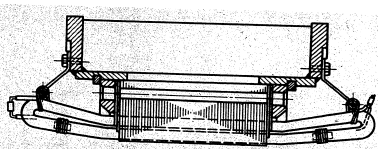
Крепление сердечника статора в станине и крепление обмотки статора
